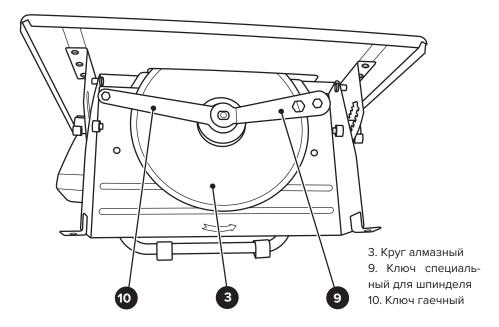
Установка и крепление алмазного круга на шпинделе станка
